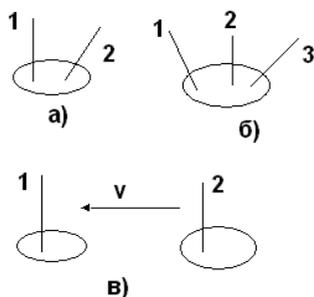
Схемы разновидностей автоматической сварки: а – двухдуговая сварка в общую сварочную ванну; б – трехдуговая сварка в общую сварочную ванну; в – сварка разнесенными дугами
